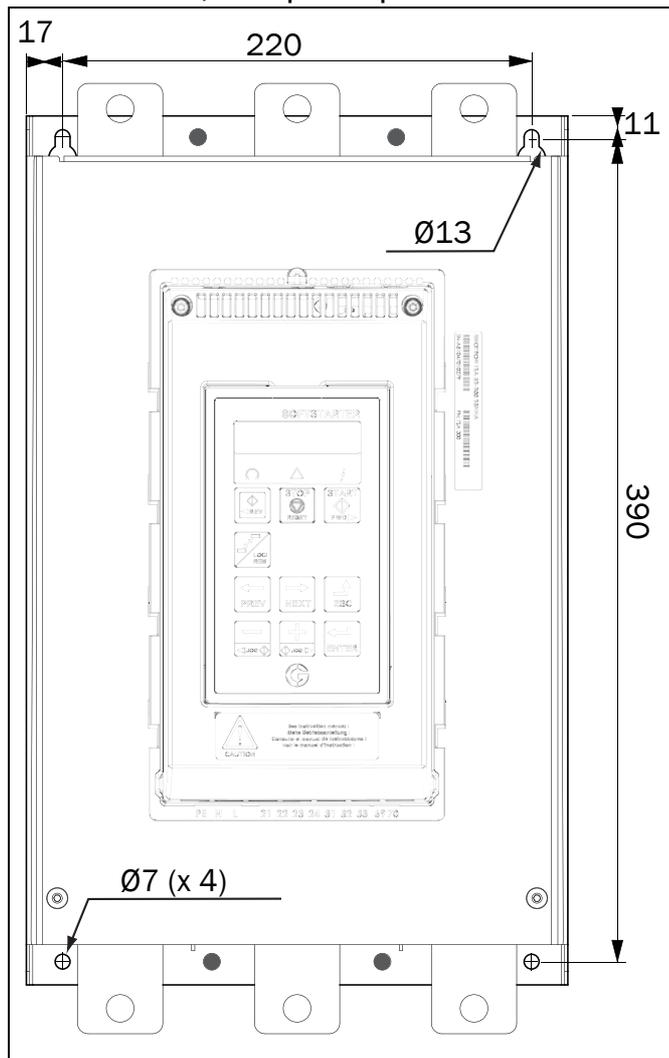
Расположение отверстий Emotron TSA, типоразмер 4.
